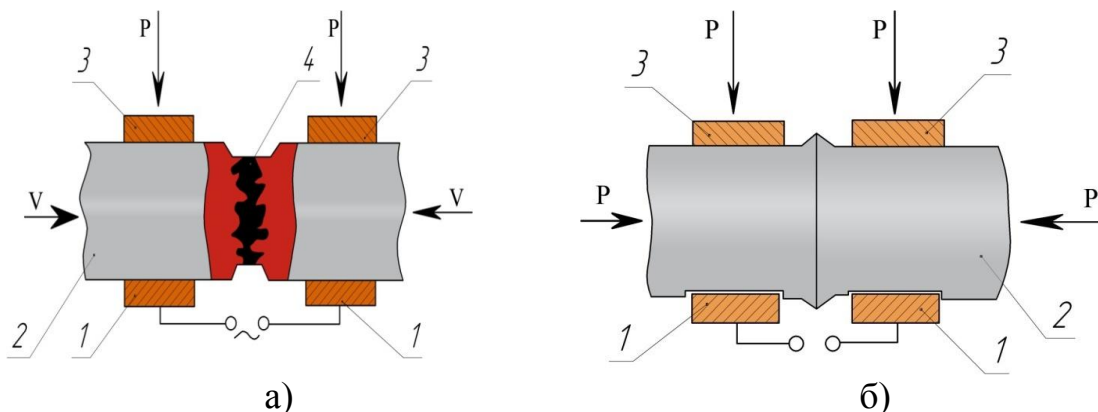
Схема стыковой сварки оплавлением: а – процесс сварки; б – после сварки; 1 – контактные губки; 2 – свариваемые детали; 3 – зажимные губки; 4 – мосты жидкого металла в контакте; 5 – грат
